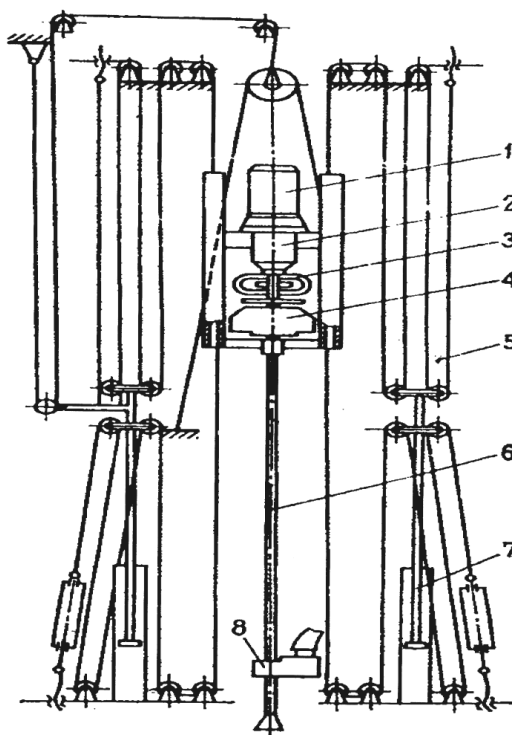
Кинематическая схема вращательно-подающего механизма станка СБШ-250МН-32: 1– электродвигатель постоянного тока; 2- редуктор вращателя; 3 – шинно-шлицевая муфта; 4 – опорный узел; 5- четырехкратная канатно-полиспастная система подачи; 6 – колонна вращающихся штанг; 7 – гидроцилиндр подачи; 8 – механизм свинчивания-развинчивания штанг
